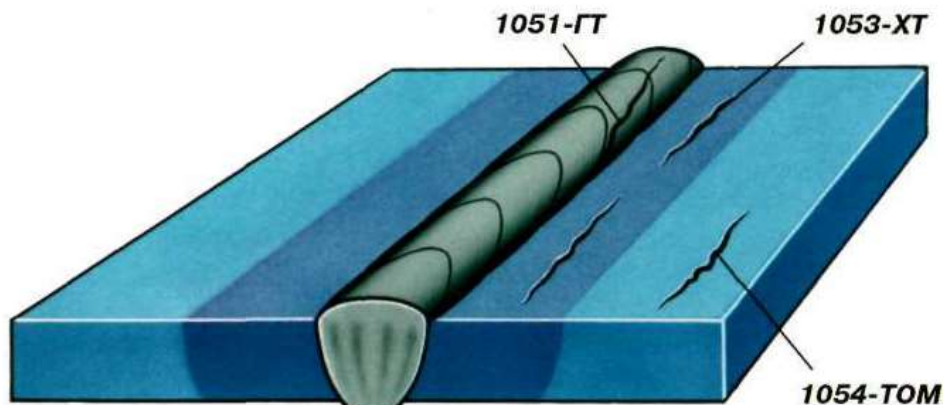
Дефекты сварного шва по типу отдельных трещин
